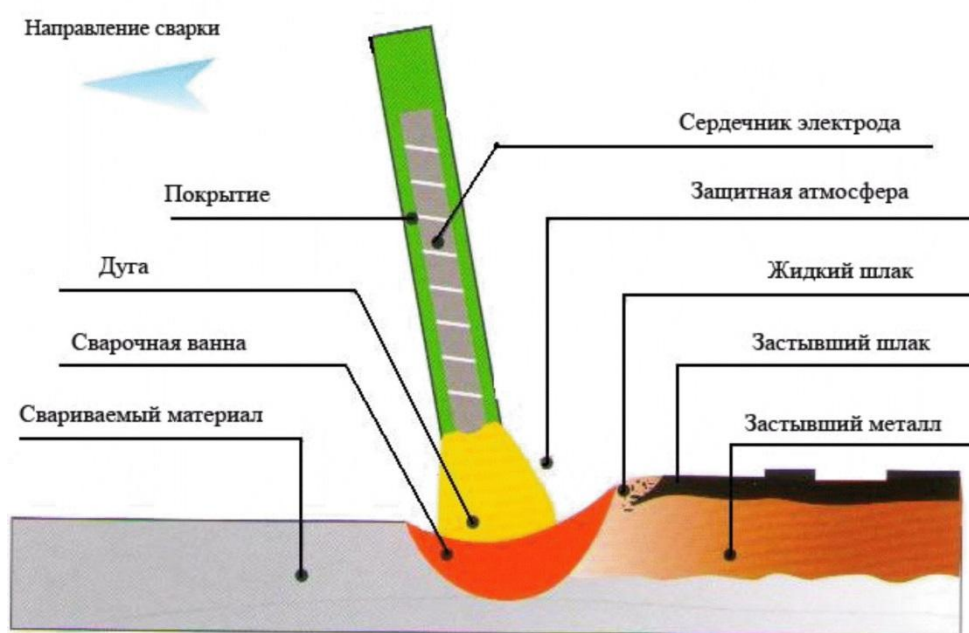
Схема ручной дуговой сварки штучными электродами
